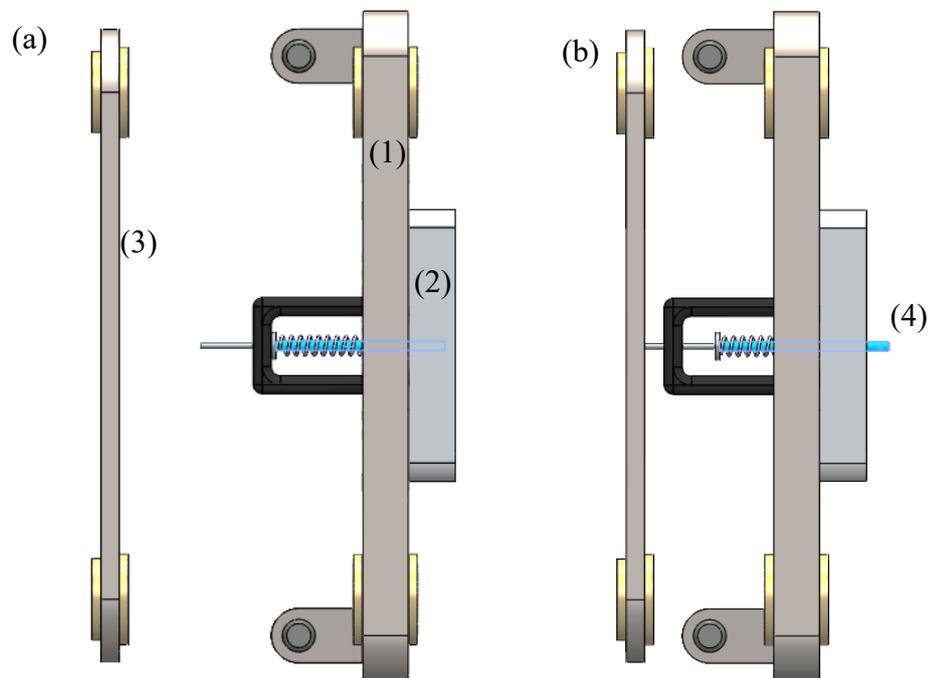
Sistema de extração: (a) recuado e (b) acionado. (1) placa móvel, (2) molde, (3) placa extratora e (4) pino extrator avançado
